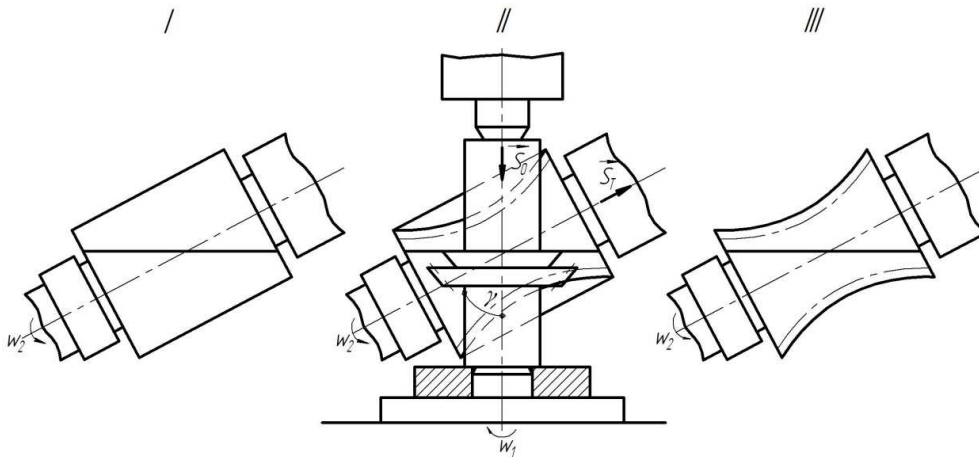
Схема изготовления гиперболического зубчатого колеса
